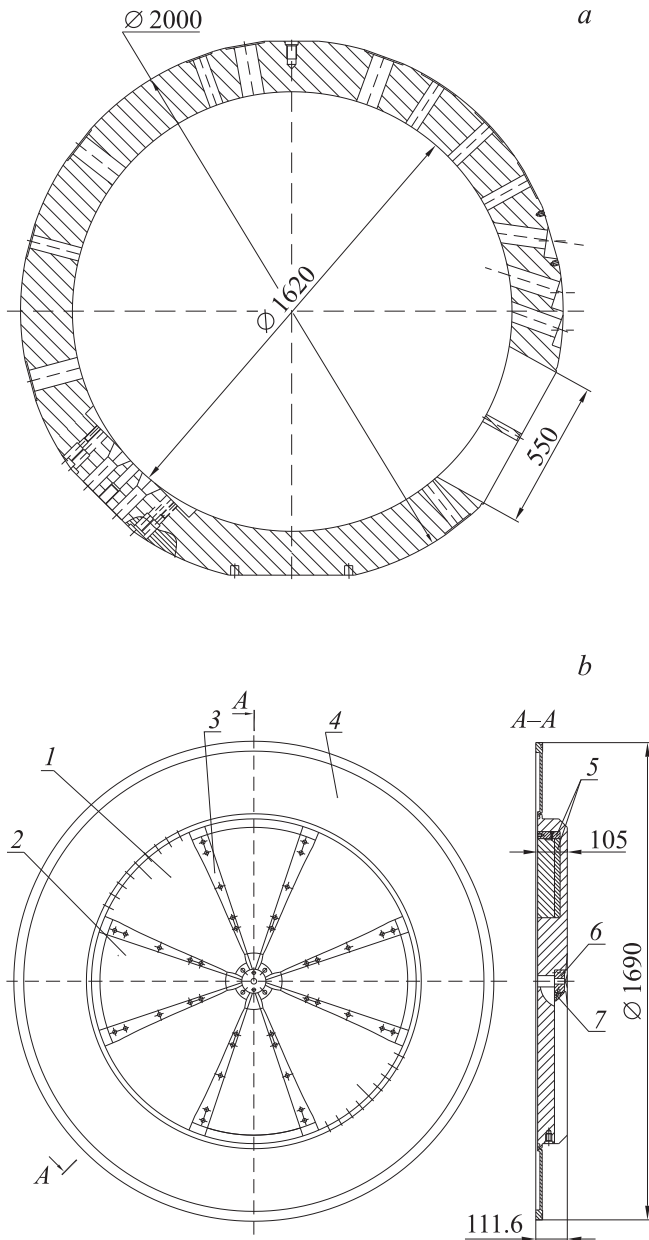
a* — типичное поперечное сечение магнитопровода (корпус камеры), *b* — типичный полюсный наконечник (общий вид); 1 — полюсный наконечник, 2 — сектор, 3 — боковой шимм, 4 — кольцевая пластина, 5 — подвижный шимм, 6 — магнитная пробка, 7 — центральный шимм.
